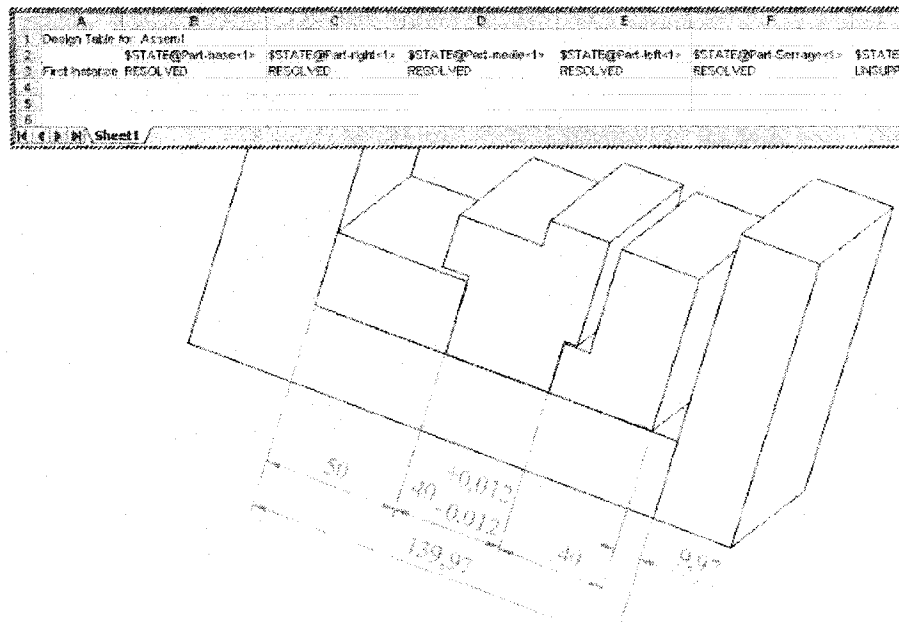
Design Table de SolidWorks pour un assemblage
